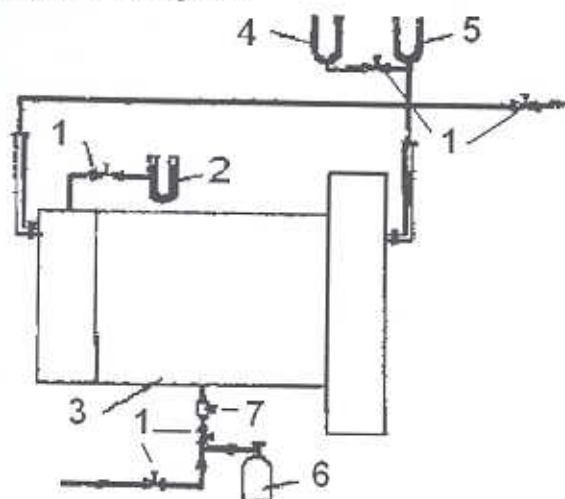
Схема определения мест утечки в корпусе статора в сборе:
